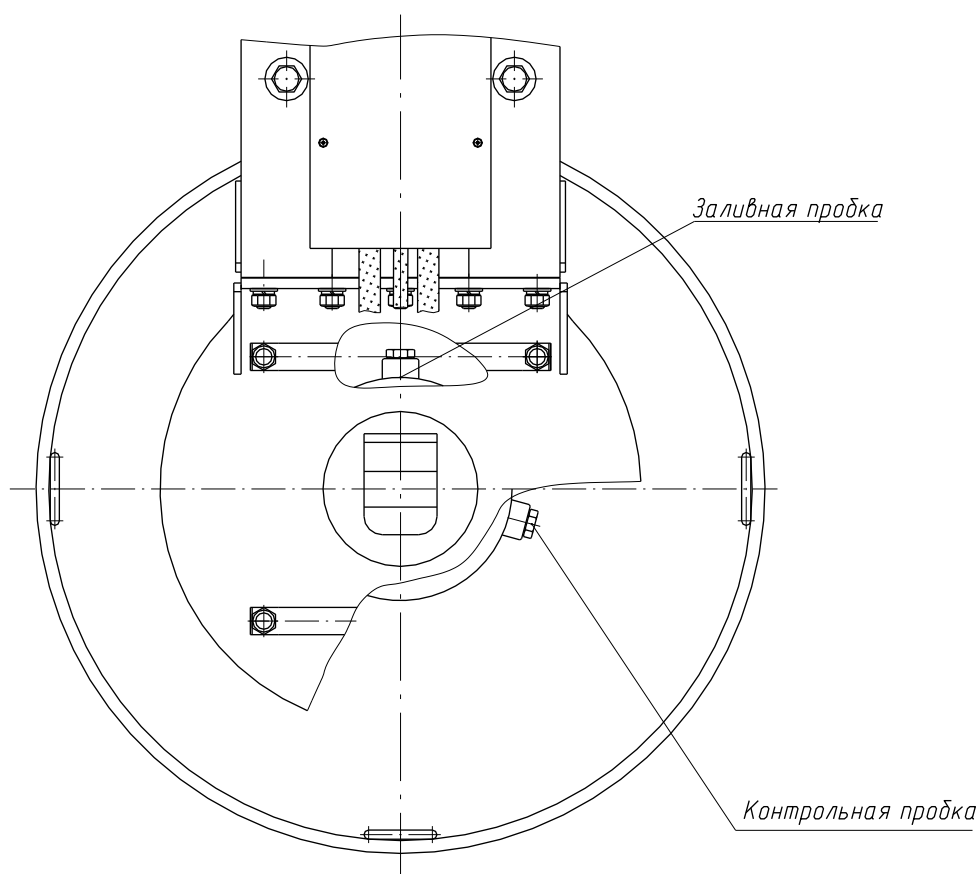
Схема расположения пробок для слива масла из полости вибратора и контроля уровня масла в вибраторе
